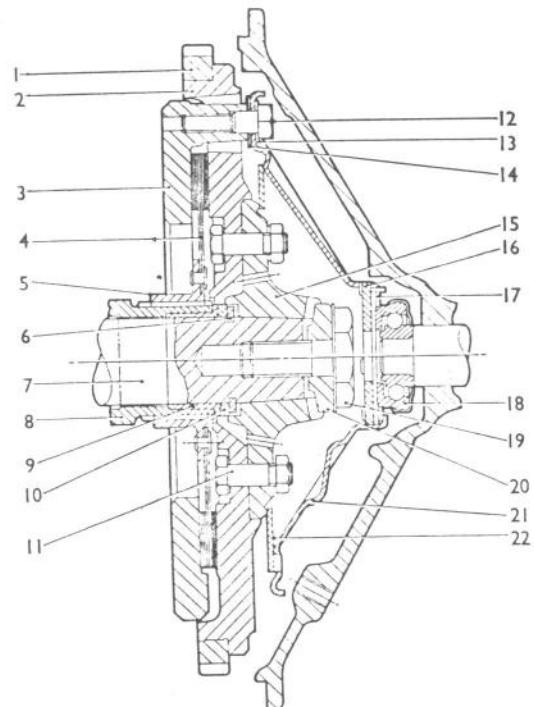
Sección en el volante del motor y en el embrague del diafragma.
